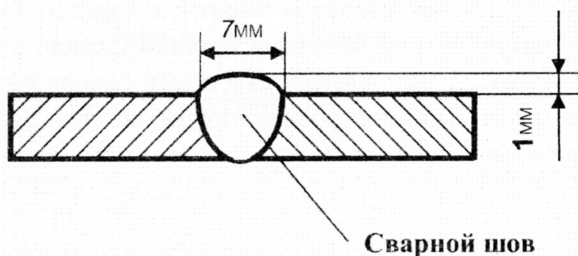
Вид сварного соединения дуговой сваркой в защитном газе неплавящимся электродом с присадкой или плавящимся электродом
